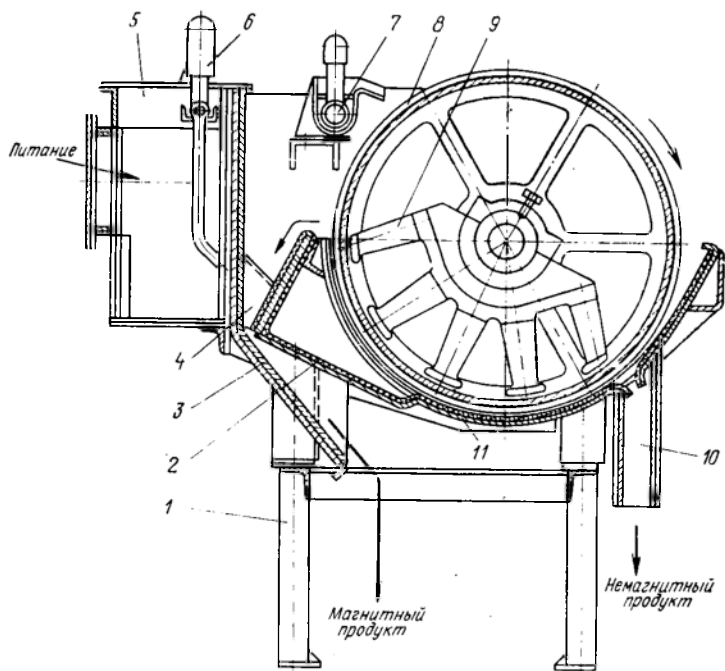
Противоточный магнитный барабанный сепаратор ПБМ-80/250
